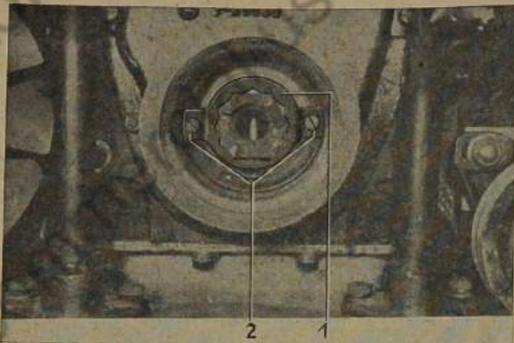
Sicherungsblech für Andrehklaue abschrauben
